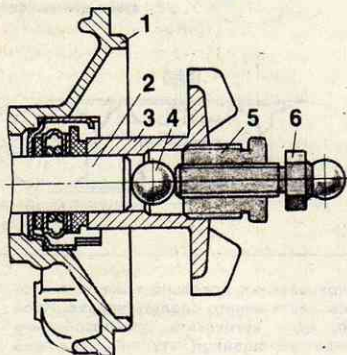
Съёмник крыльчатки из деталей собственного мотора: 1 — крышка водяного насоса; 2 — валик; 3 — крыльчатка; 4 — шарик; 5 — ступица регулировки клапана; 6 — регулировочный болт.
